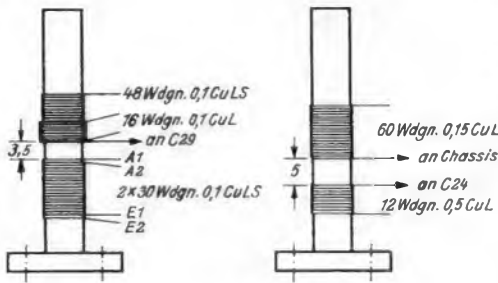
Die beiden Tonfilter, links Diskriminatorfilter
